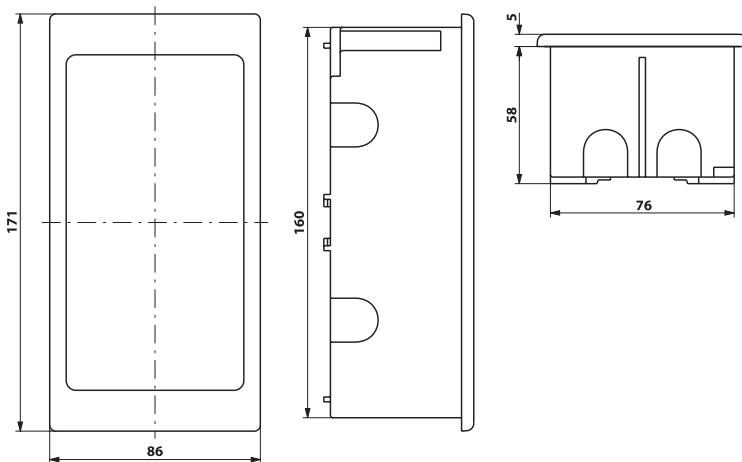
MK 2430 en carcasa de montaje bajo pared
